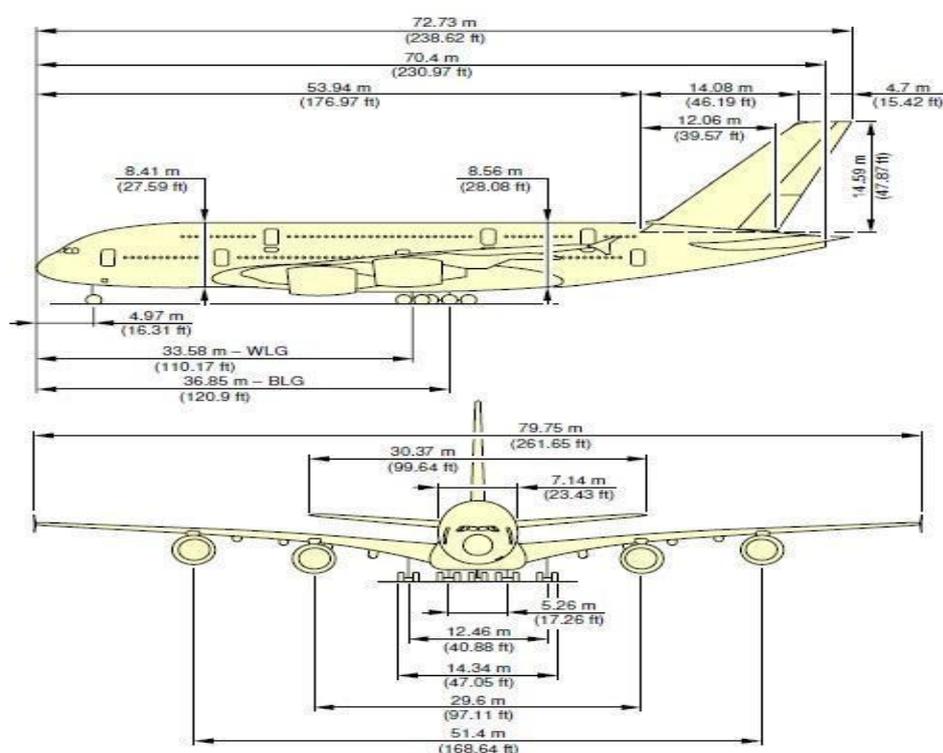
Dimensions de l'A380-800 (1). [5]
